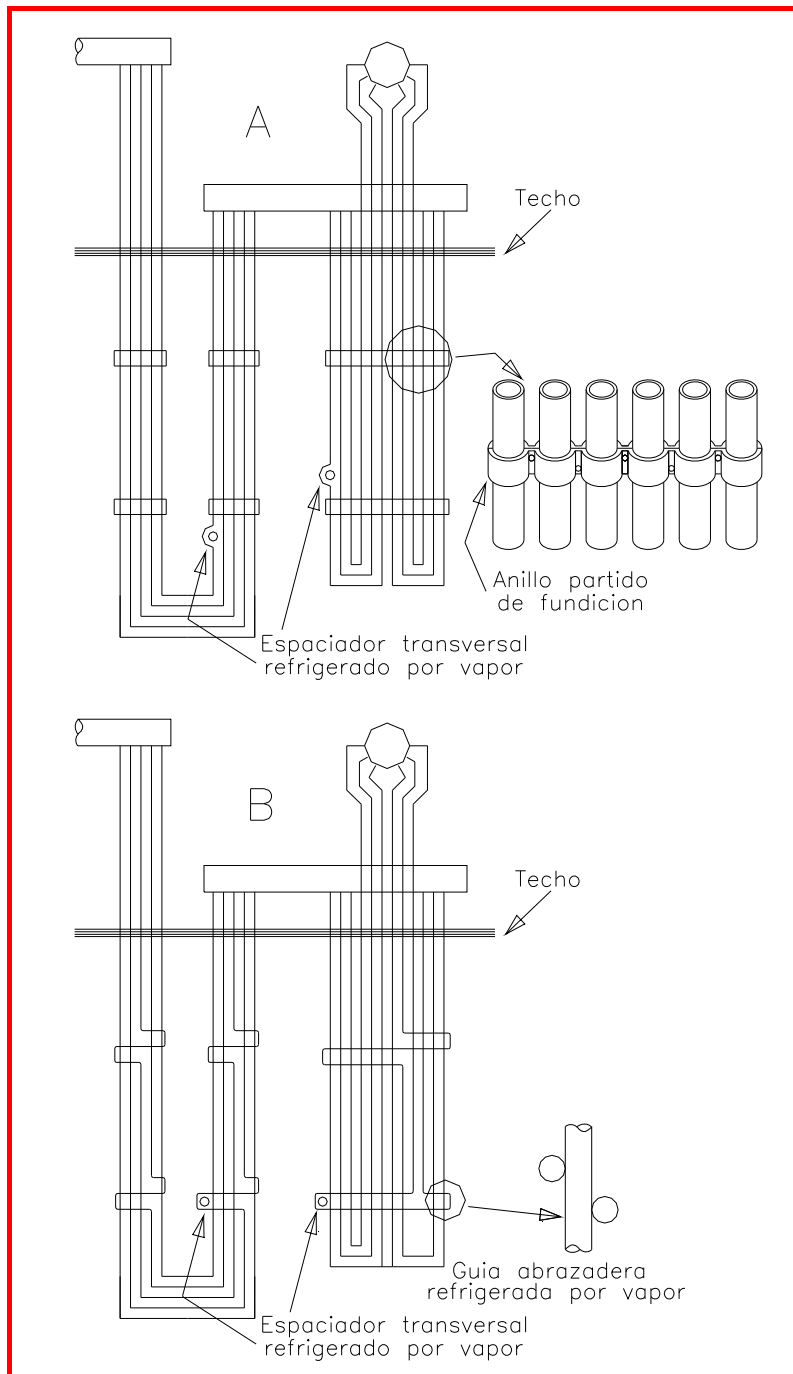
Disposiciones con soportes estándares, para la sección de salida de un sobrecalentador vertical, con soportes de la sección principal situados encima del techo de la caldera
